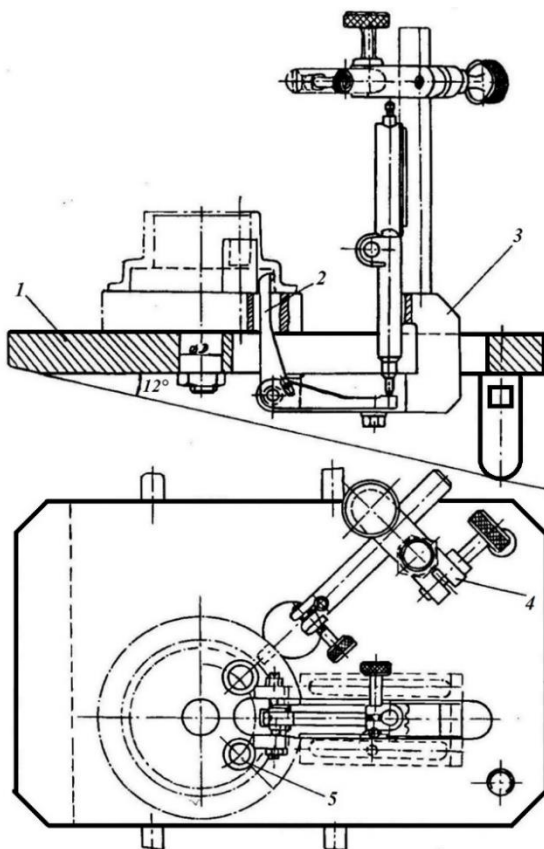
Приспособление для контроля биений диаметров деталей типа «втулка»
